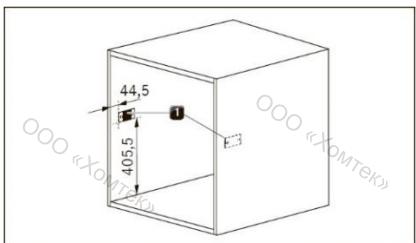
Установочное углубление с монтажными пластинами корпуса
